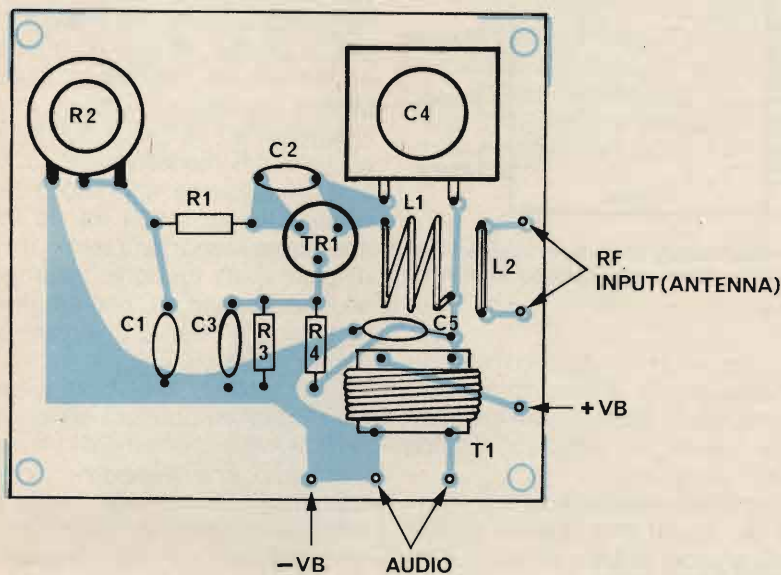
Basetta a circuito stampato e disposizione dei componenti.
